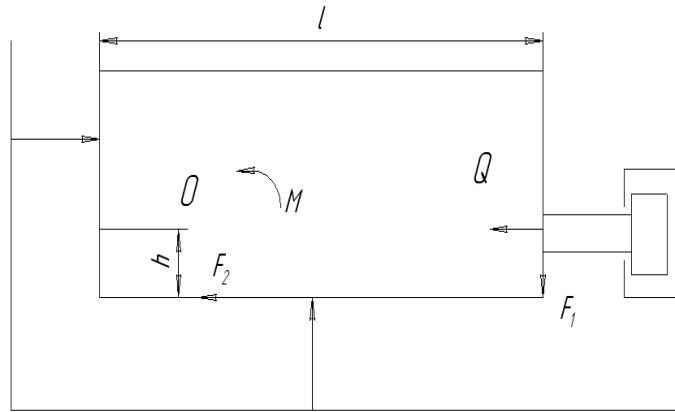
Схема для розрахунку зусилля затиску коробки передач
